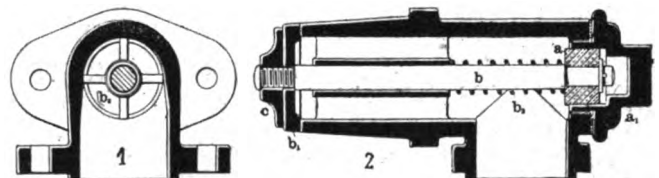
Einlassventil der Springfield Gas Engine Company.
